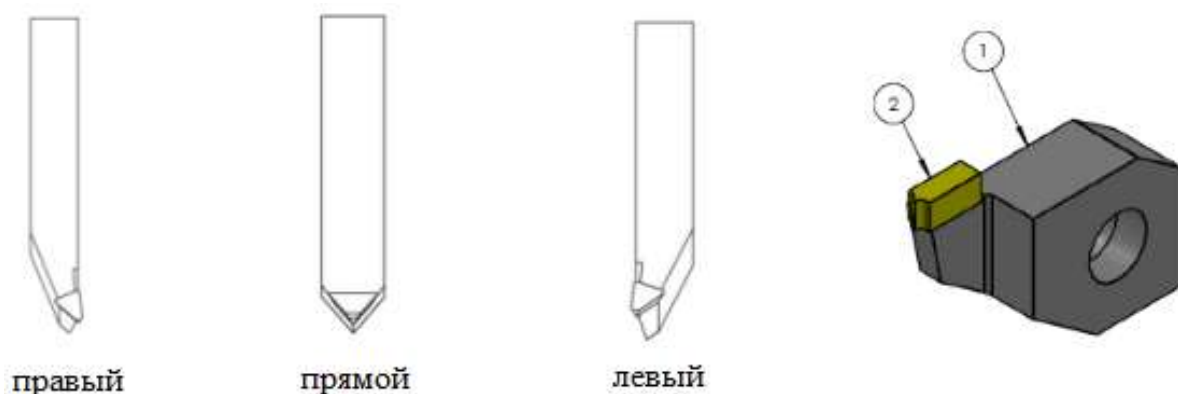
Чертежи различных видов резцов используемых для точения микрорезонаторов.
